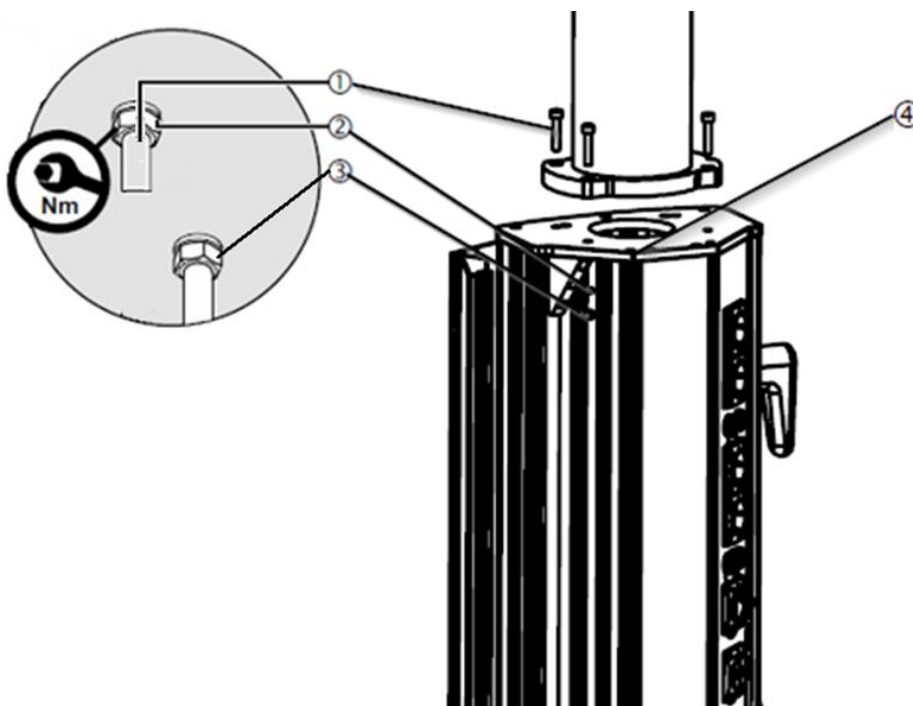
Desmontaje / montaje del cabezal de servicio sobre el tubo de caída.
